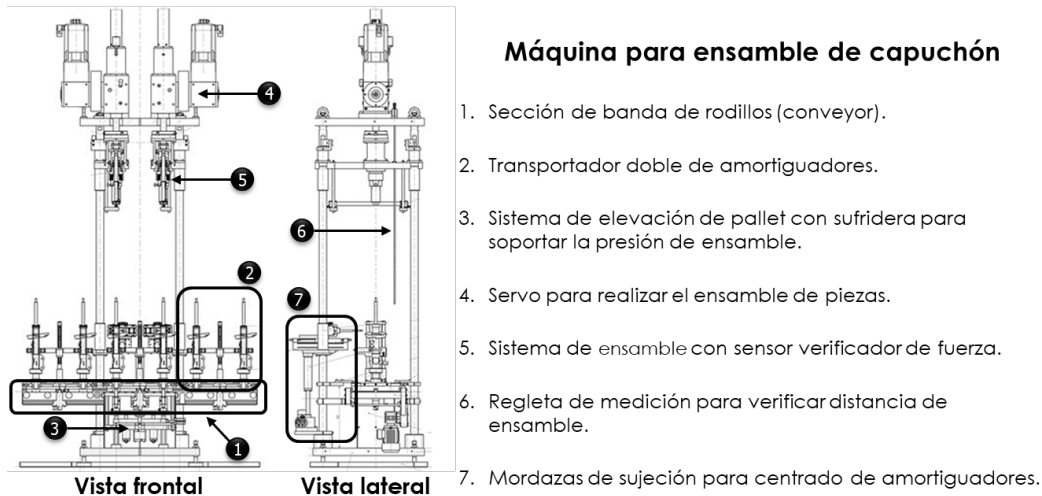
Máquina para el ensamble de capuchón en línea modular.
